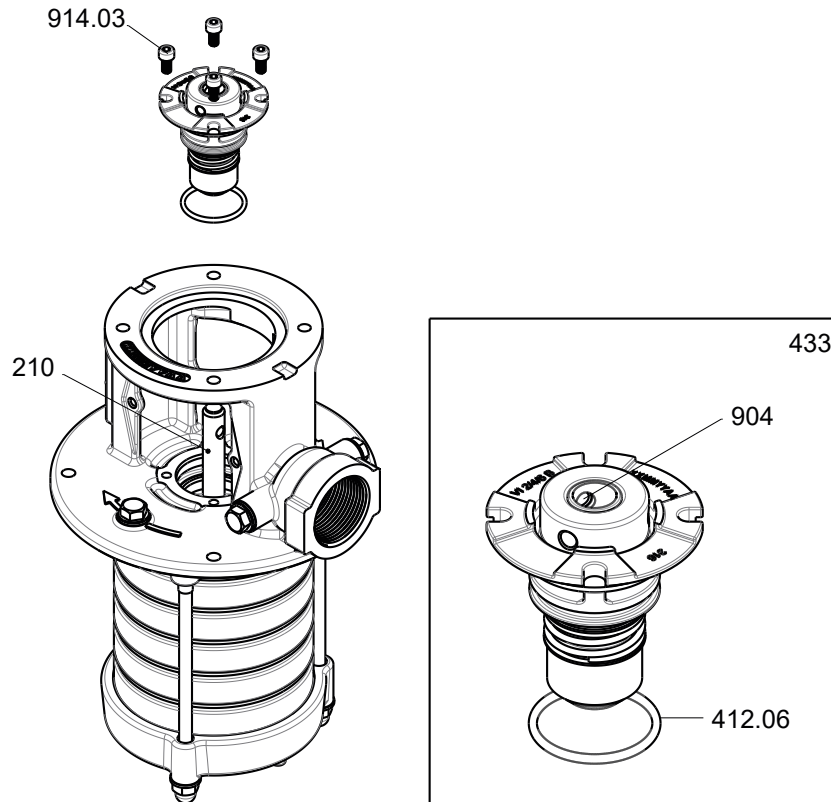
[TPG-20120136-C]: Gleitringdichtung ausbauen
